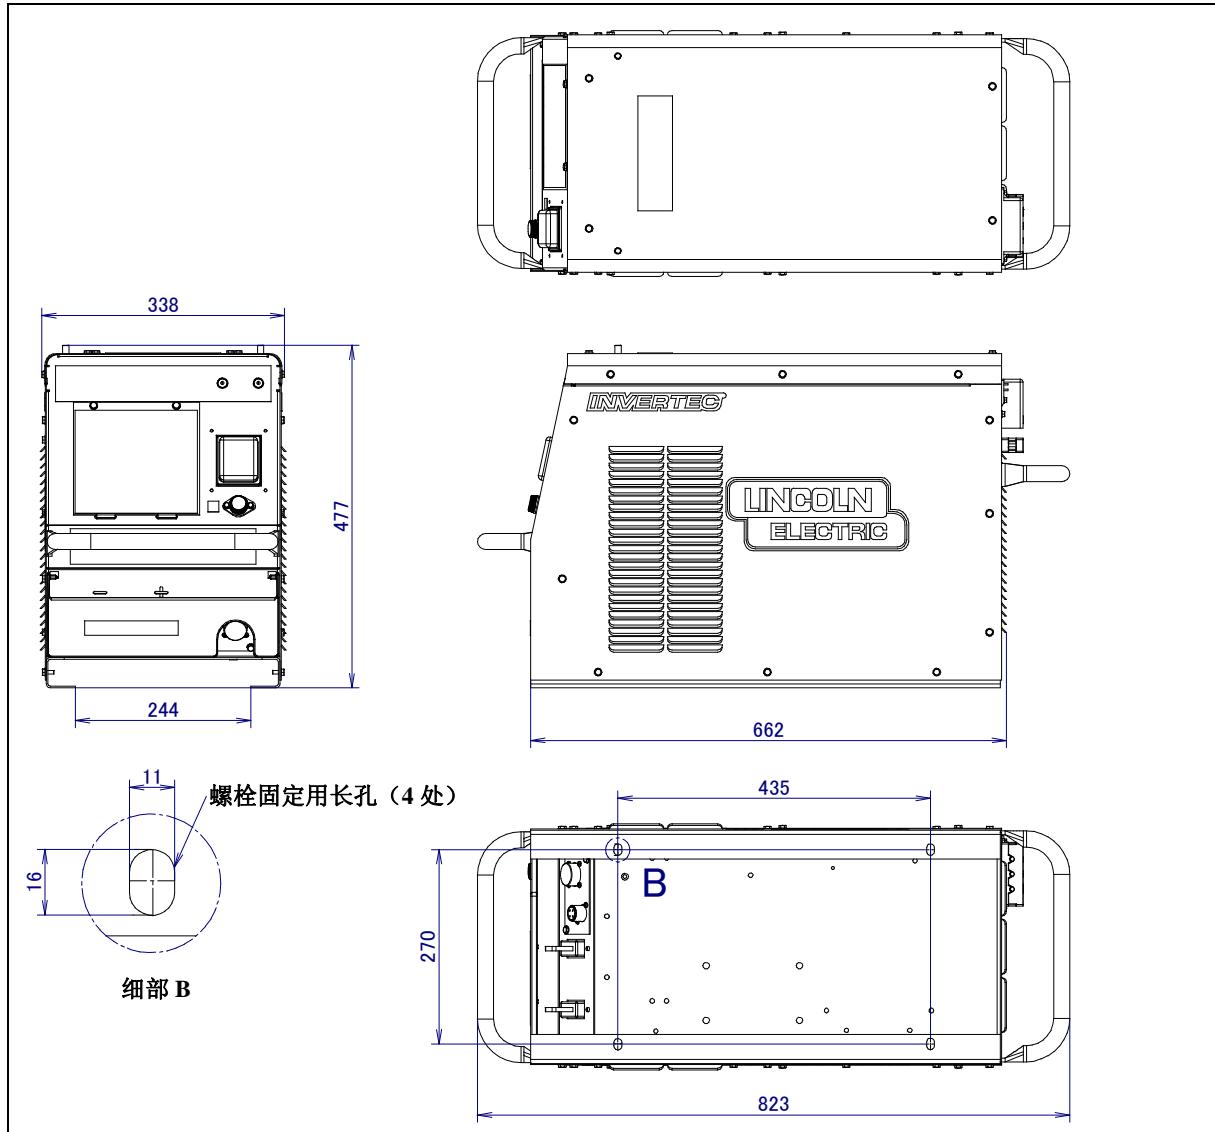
(c) ROBOWELD iC/E 用焊接电源 (CV350-R)
